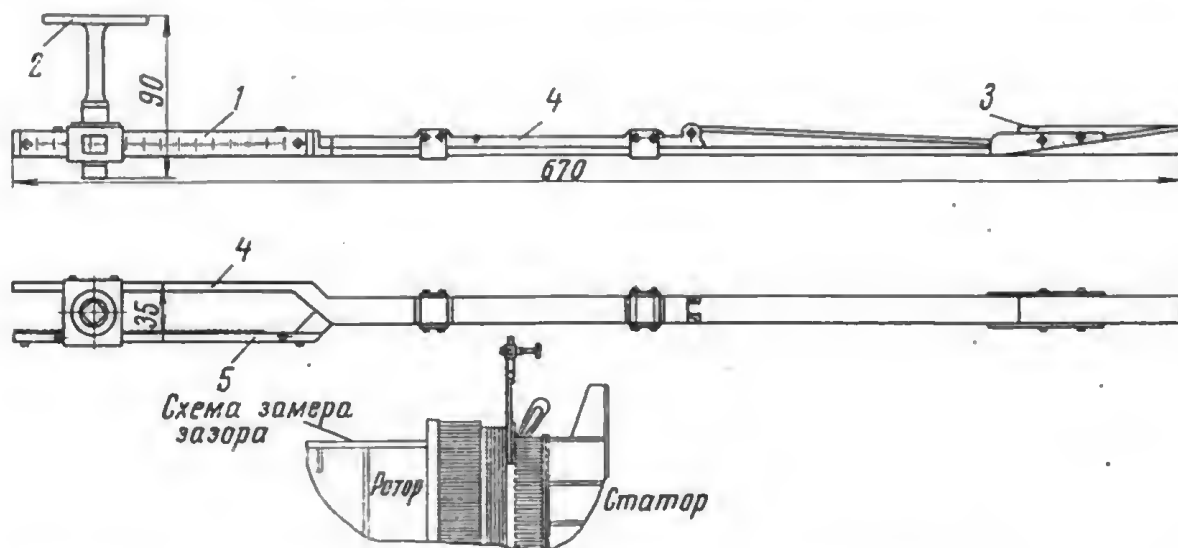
Приспособление для измерения воздушного зазора генератора.
